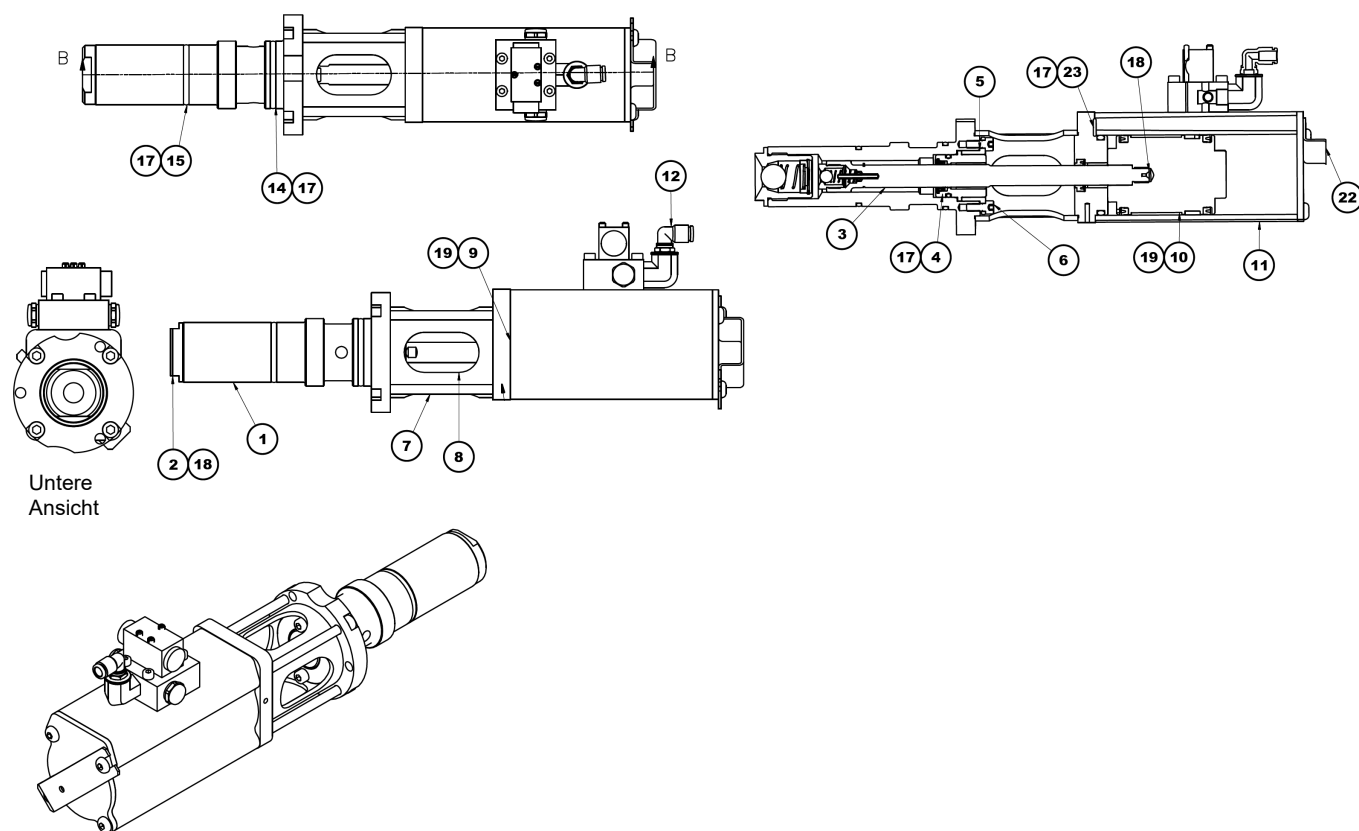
Baugruppe pneumatische Kolbenpumpe, Art.-Nr. 150039
